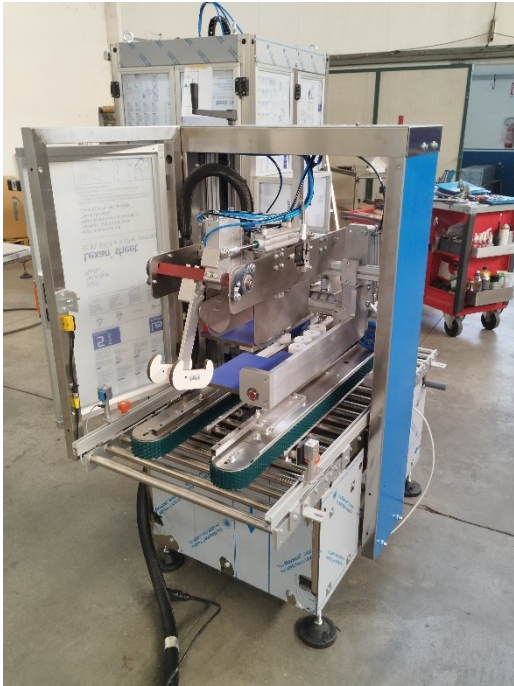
Modifica della parte posteriore delle lamiere di supporto di parte del meccanismo di chiusura falde
